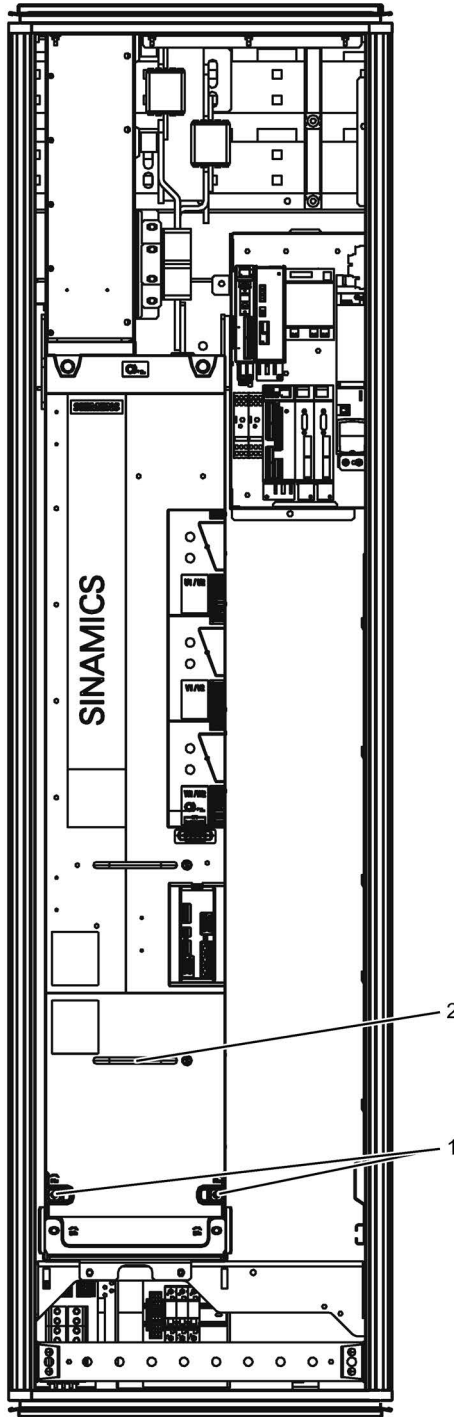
Замена вентилятора, модуль двигателя «шасси-2», типоразмер FS4
